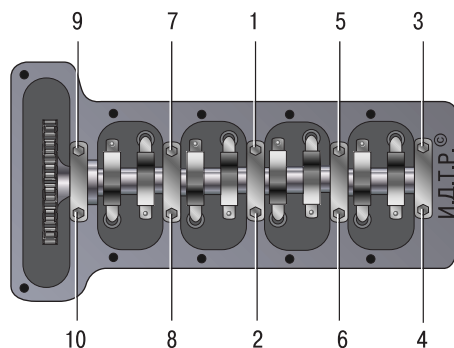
Порядок затяжки болтов крышек подшипников распределительного вала двигателя Duratec объемом 1,3 л
